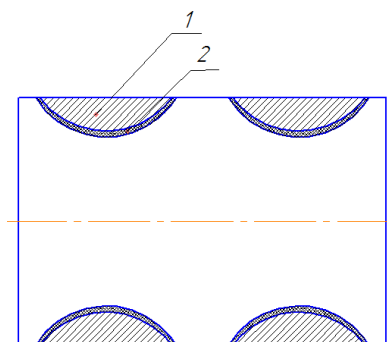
Схема зона черновой и чистовой обработки: зона 1 –черновая обработка; зона 2 – чистовой обработки
